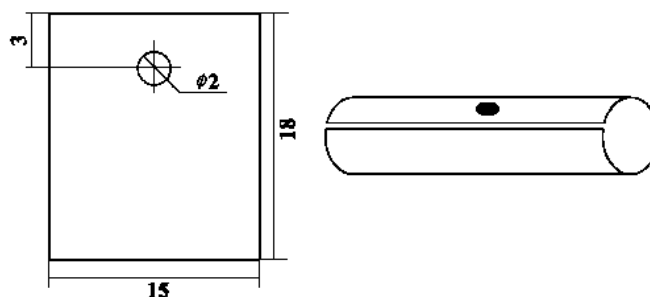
Форма и размеры заготовки из танталовой фольги
